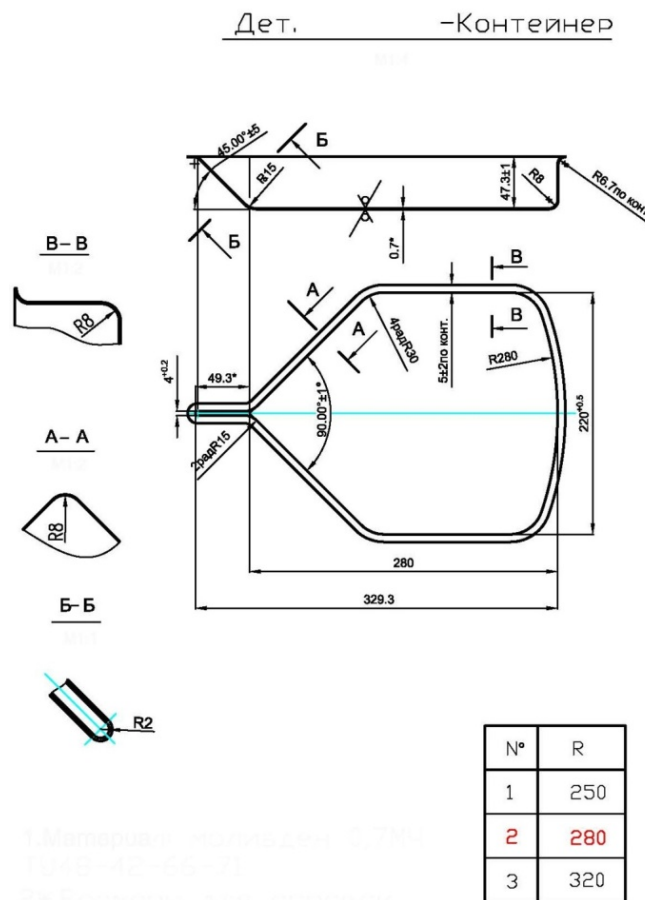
Рабочий чертеж контейнера-лодочки
